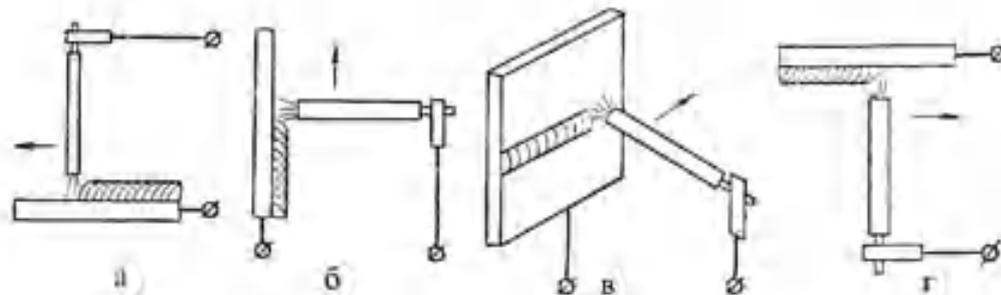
Возможные пространственные положения шва при ручной электродуговой сварке:
